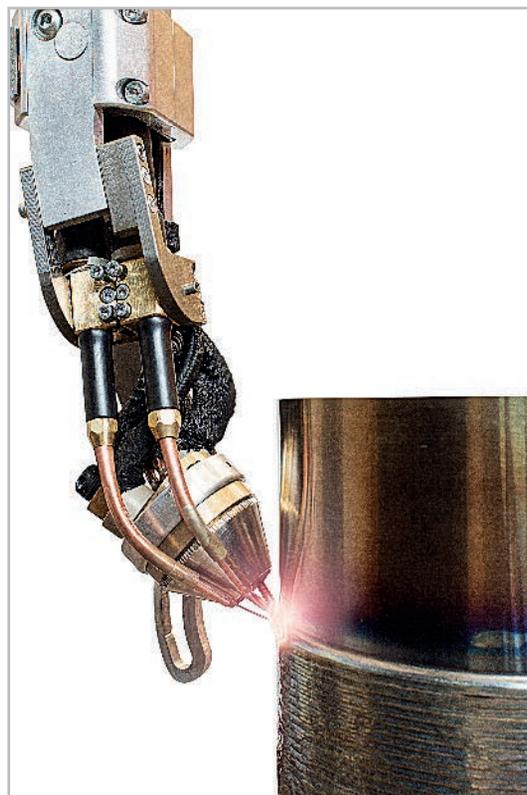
Наплавочная горелка Speed Clad Twin от Fronius
